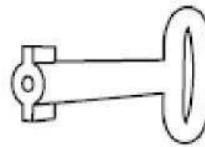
Llave de doble paletón (Installation and Operating Instructions Medium-Voltage Switchgear) [7]
